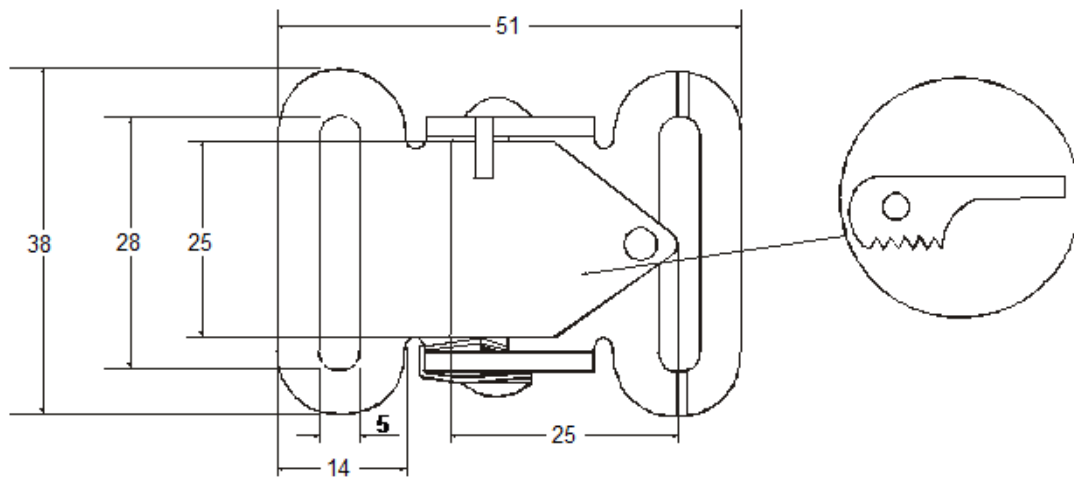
Vista do topo do ajustador metálico (medidas em mm).
